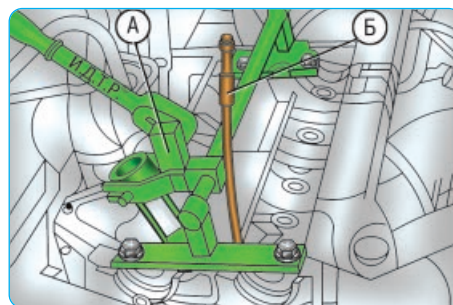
Приспособления для снятия пружин клапанов: А – приспособление для сжатия пружин; Б – приспособление для подачи воздуха в свечное отверстие
